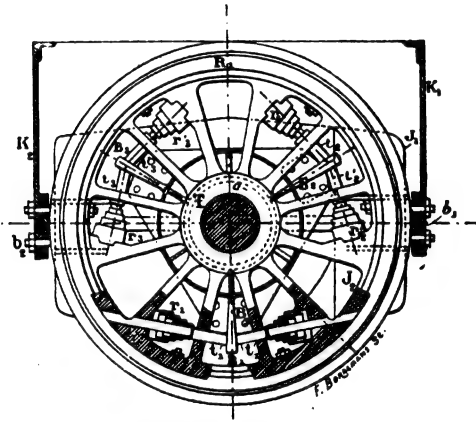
Vue de face d'un essieu du côté de la roue motrice.
